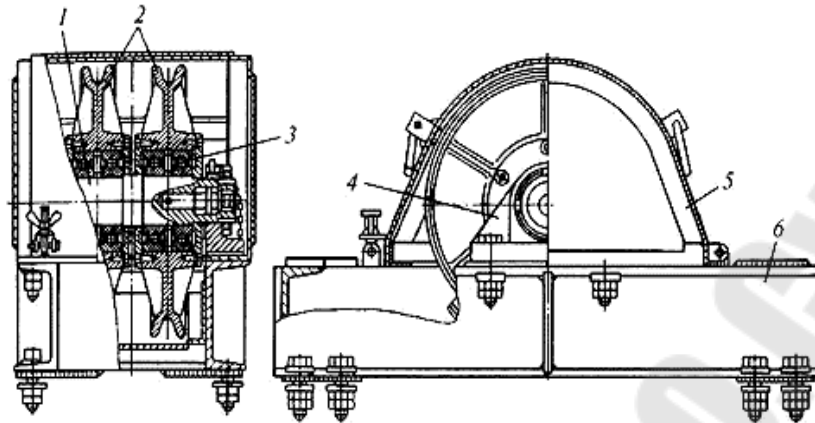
Внешний вид кронблоков буровых установок: 1-ось; 2-шкивы; 3-подшипники качения; 4- опора подшипника; 5- кожух; 6- рама
